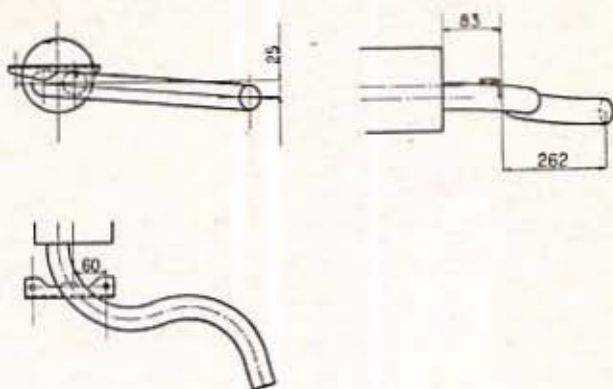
Cotes de soudures du support de tuyau
